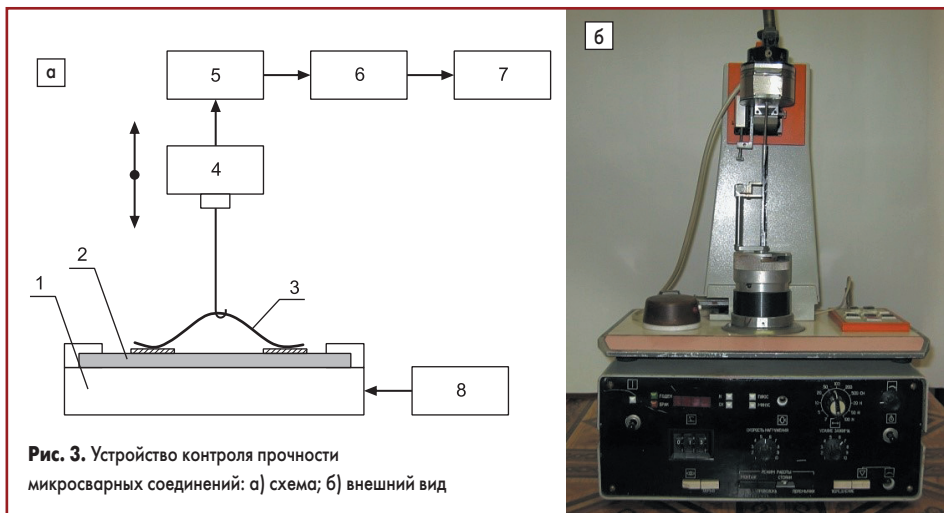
Устройство контроля прочности микросварных соединений: а) схема; б) внешний вид
